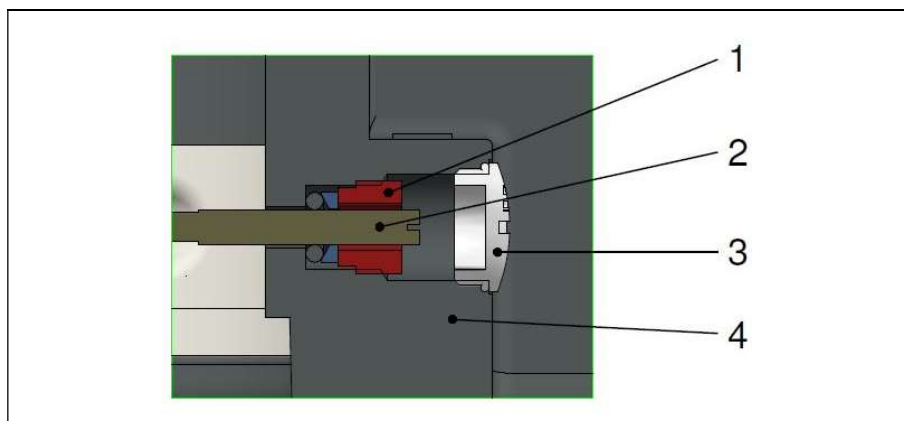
Pièces de réglage de la soupape de levage/d'abaissement
